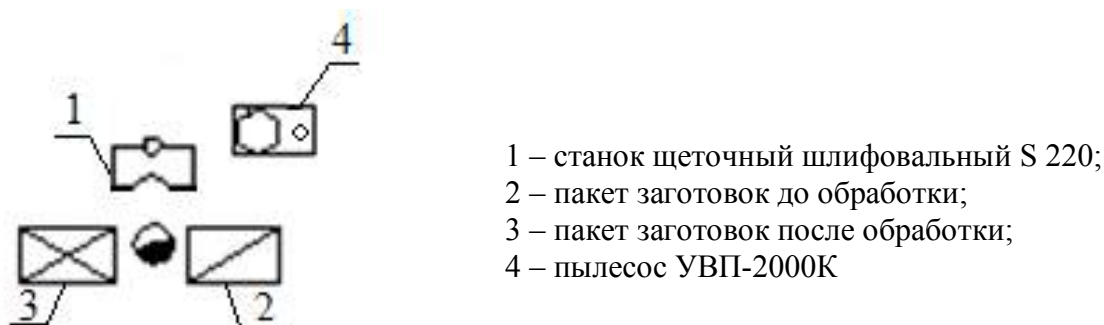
План рабочего места у щеточного шлифовального станка S 220
